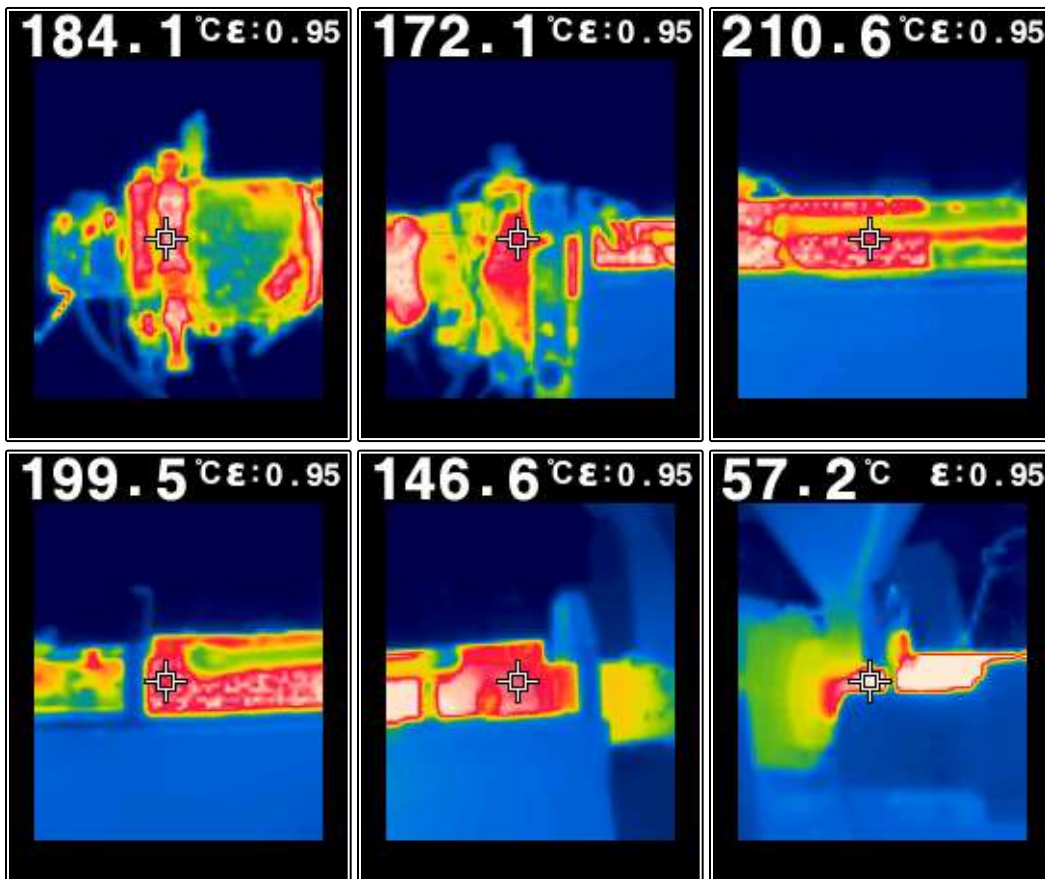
15: Termofotografías de varios segmentos de la extrusora (de izquierda a derecha): a) el cabezal de extrusión, b) la conexión con el barril, c) zona de compresión, d) zona de fusión, e) zona de transporte y f) zona de alimentación.
